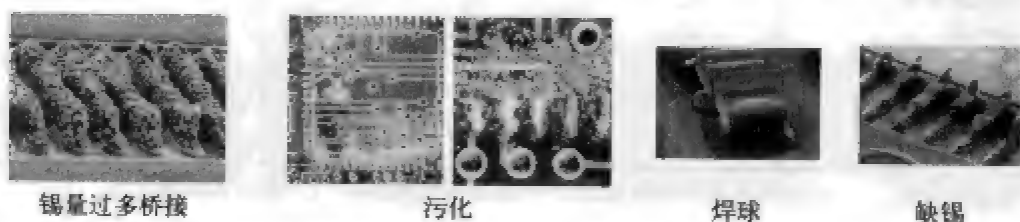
焊膏印刷工艺引起的焊接缺陷
